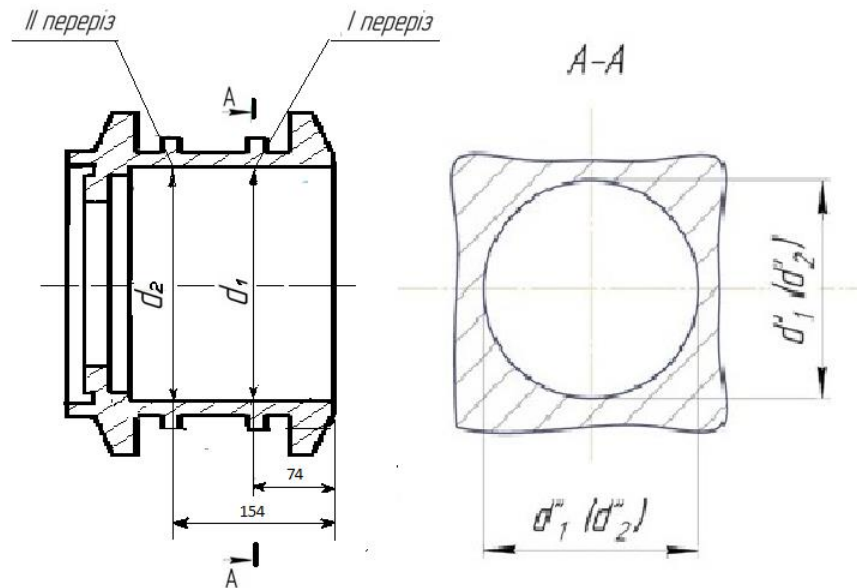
Вимірювання діаметра внутрішньої циліндричної частини корпусу букси
